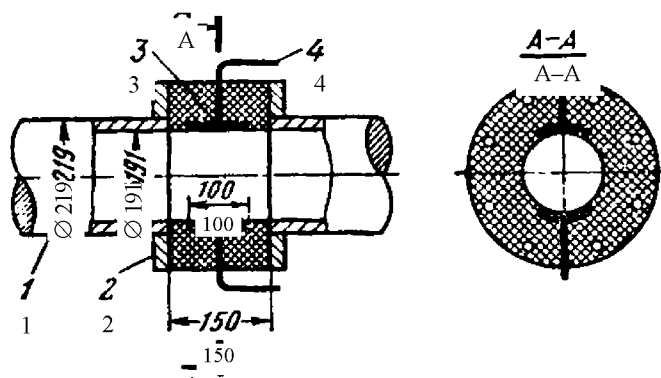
Схема устр. А для индикатора движения закладочной смеси
